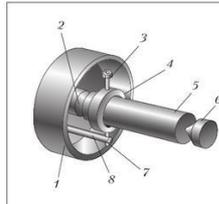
Установка заготовки с помощью поводковой планшайбы: 1 – корпус планшайбы; 2 – передний центр; 3 – стопорный винт; 4 – контргайка; 5 – заготовка; 6 – задний центр; 7 – стержень; 8 – поводок
